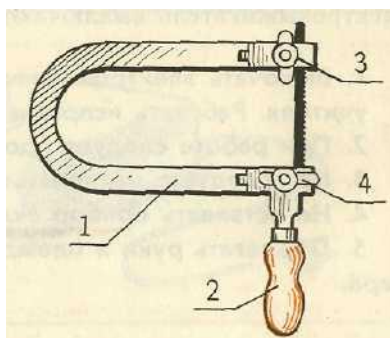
Лобзик: 1 — рамка; 2 — ручка; 3 — верхний зажим; 4 — нижний зажим
